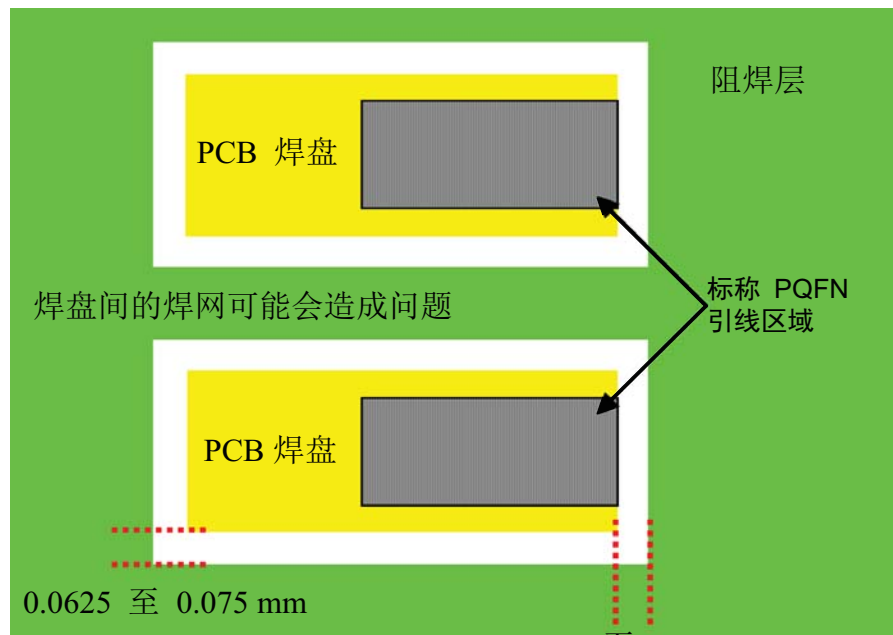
周缘采用阻焊层的 PCB 焊盘上的 PQFN 焊盘顶视图
